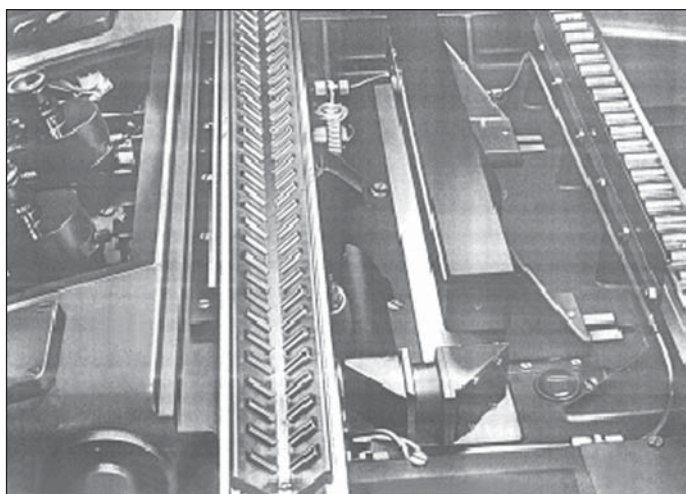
V-образная и плоская роликовые направляющие стола координатно-расточного станка
